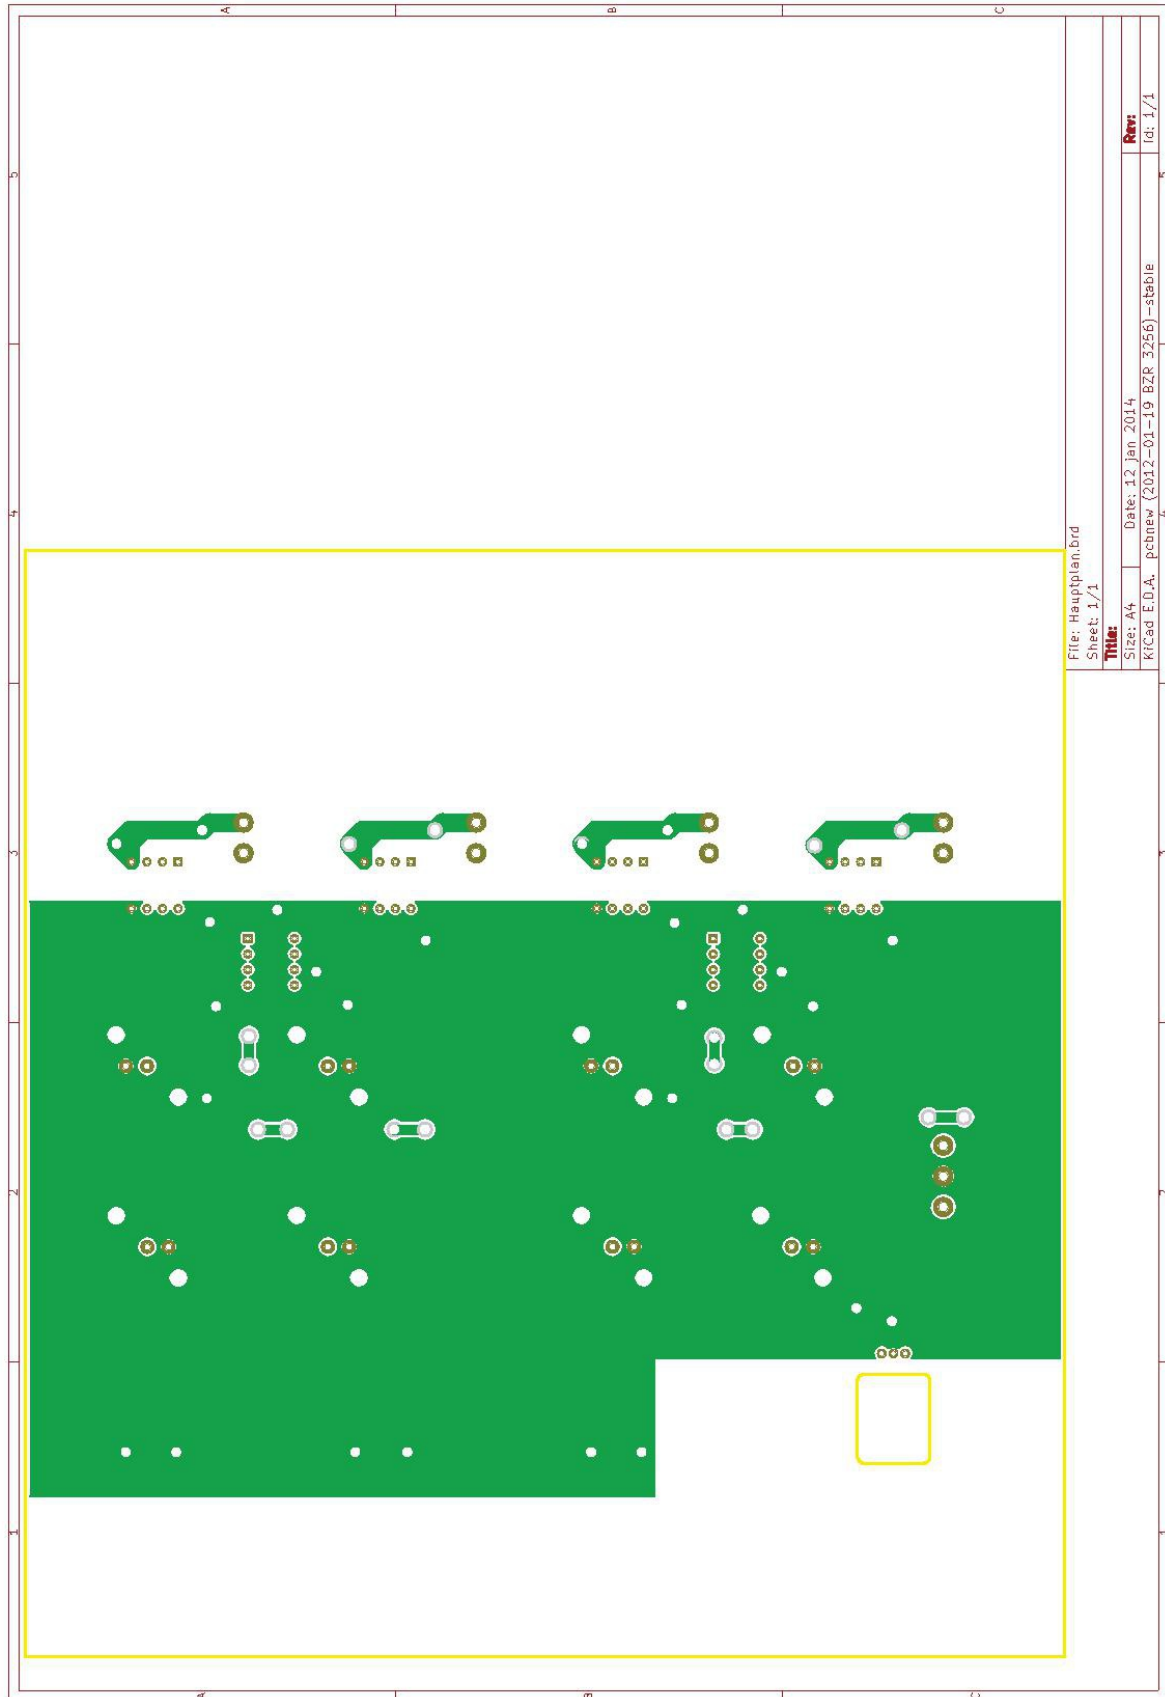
PCB-Layout Rückseite (bottom) der Gruppierungen 3 bis 6
